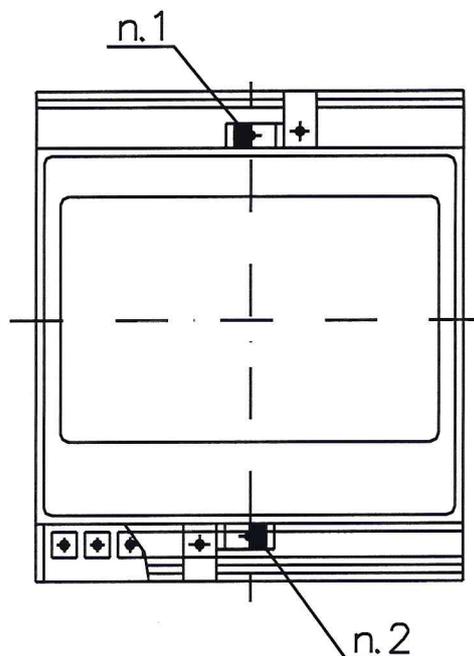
Общий вид и маркировка ИП E858/12 для нужд народного хозяйства
